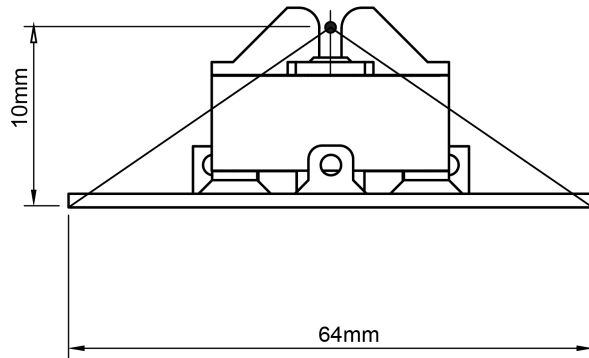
Sectional side cut: circle marks the center point of magnet with sensor pcb on the bottom
